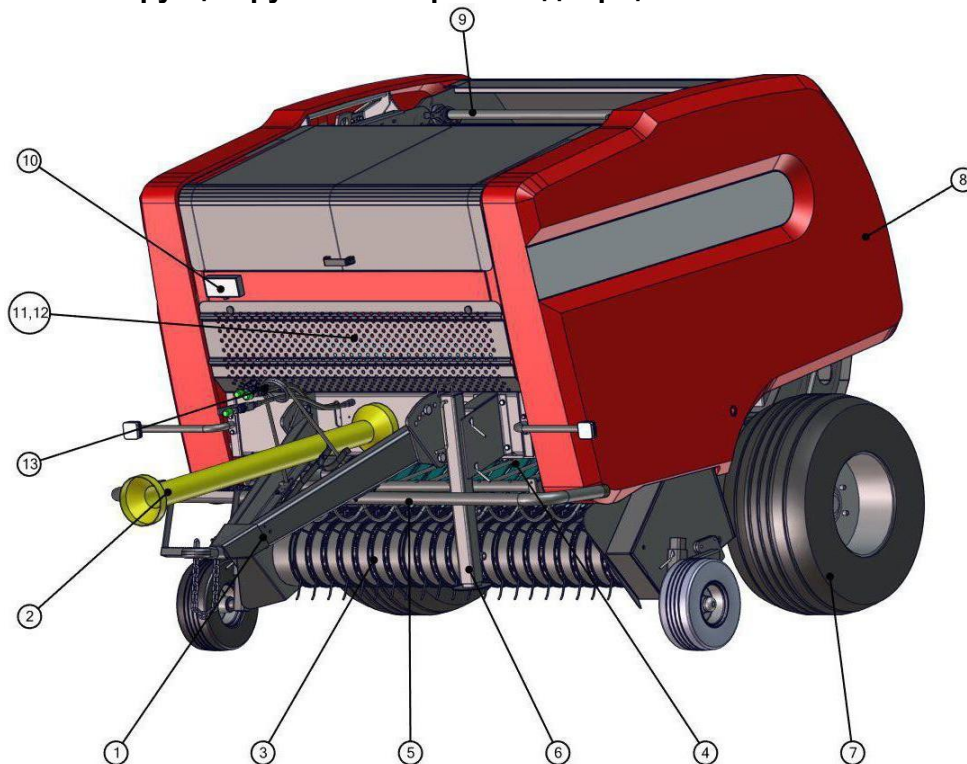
Конструкция рулонного пресс-подборщика Z587, Z587/1 (1 - Дышло; 2 – Шарнирно-телескопический вал; 3 – Подборщик; 4 – Подбрасыватель; 5 – Защитное ограждение с платформой, 6 - Опорная пята; 7 – Ходовое колесо; 8 – Защитный кожух; 9 – Цепно-прутковый транспортер; 10 – Панель управления; 11 – Механизм обмотки рулонов сеткой; 12 – Механизм обмотки рулонов шпагатом; 13 – Гидравлические питающие шланги
